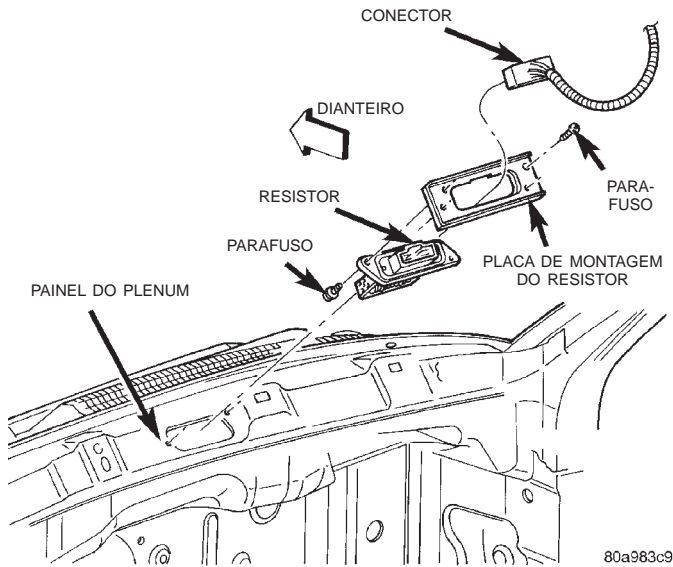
Resistor do Motor do Ventilador - Instalação de Fábrica
